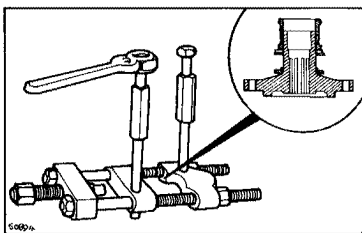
Приспособление для снятия упорной шайбы со ступицы колеса
